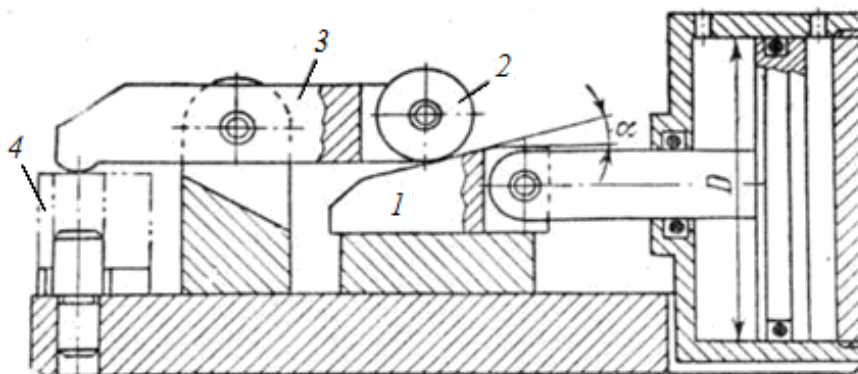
Застосування клинового затискного пристрою для закріплення заготовки
